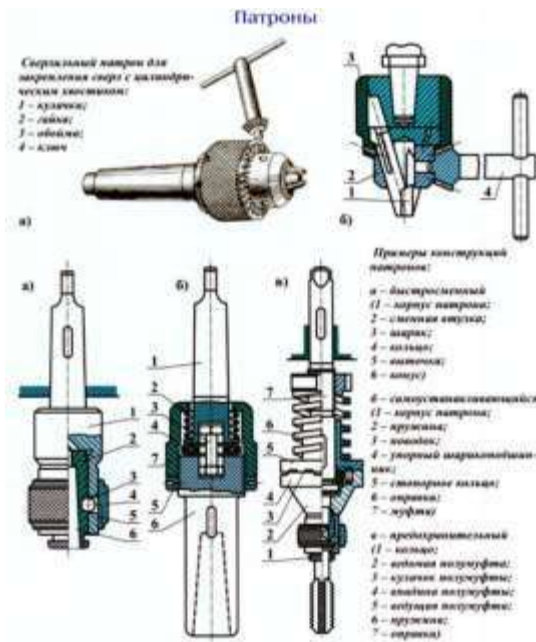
Приспособления для закрепления режущего инструмента и заготовок
